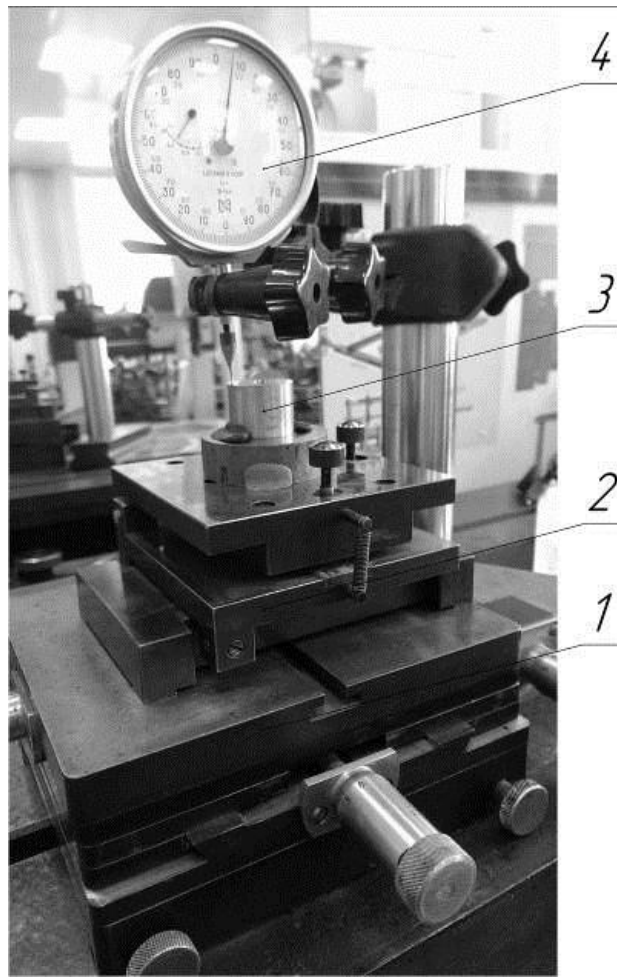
Приспособление для измерения размеров наплывов металла на торцах образцов: 1 – двухкоординатный микрометрический стол; 2 - двухповоротный стол; 3 – образец; 4 – измерительная головка
